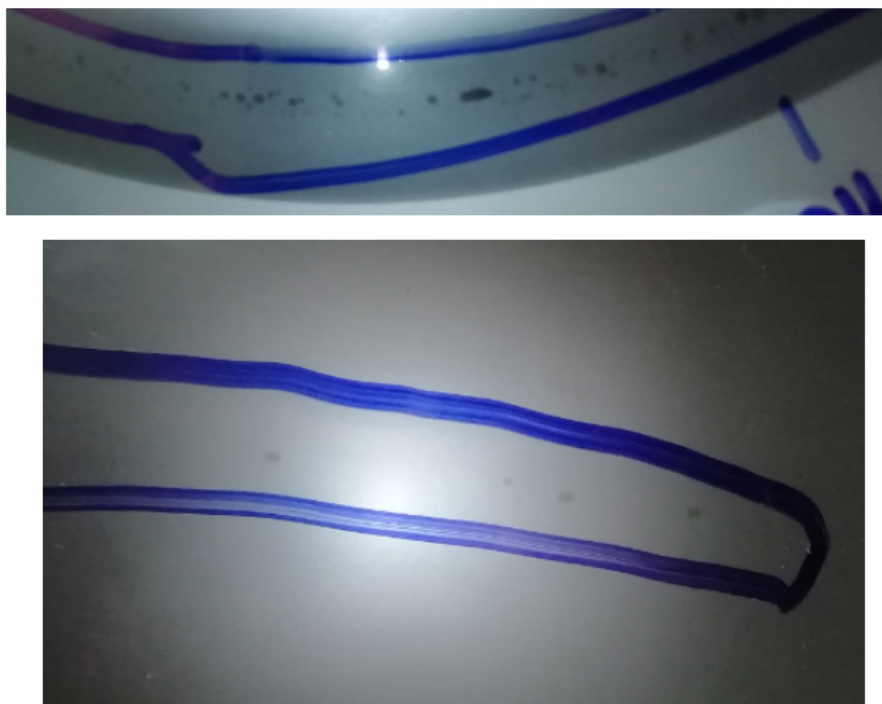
Цепочки пор на рентгенограммах сварки корпусных изделий из сплавов АМг6НН и 01570
